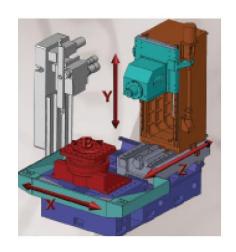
Схема сверлильно-фрезерно-расточного станка с ЧПУ 500HS
